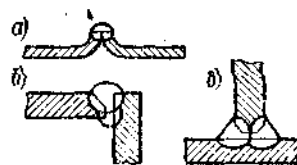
Подготовка кромок сварных швов: а - с отбортовкой кромок; б - со скосом одной кромки; в - с двумя симметричными скосами одной кромки
